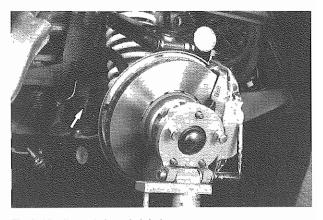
Vite fissaggio braccio inferiore Lower arm fixing screws
